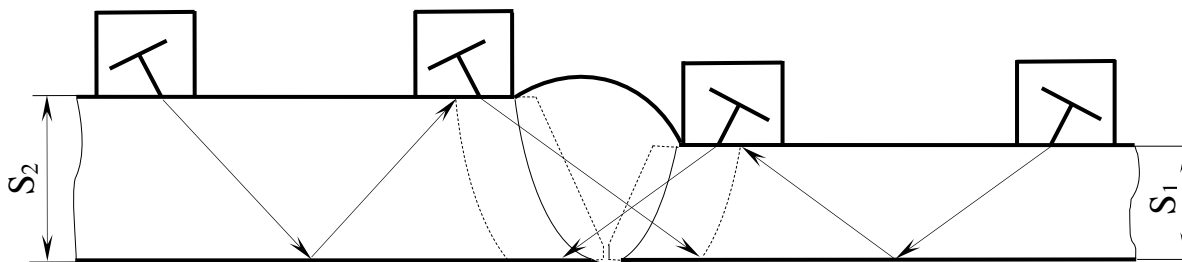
Схема контроля разнотолщинных стыковых сварных соединений
